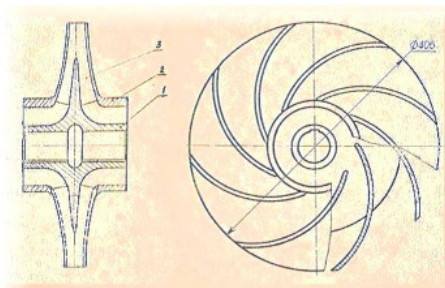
Рабочее колесо сварной конструкции центробежного насоса 6НДв
